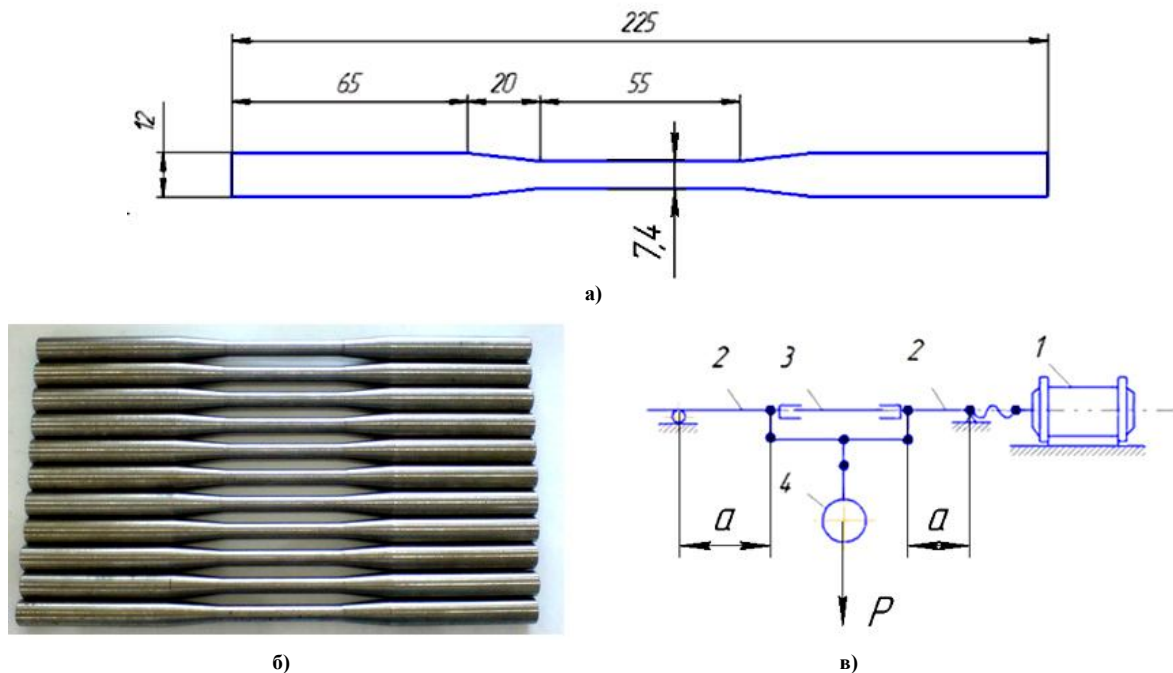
Эскиз образца (а) и фото нескольких образцов (б) для усталостных испытаний;
